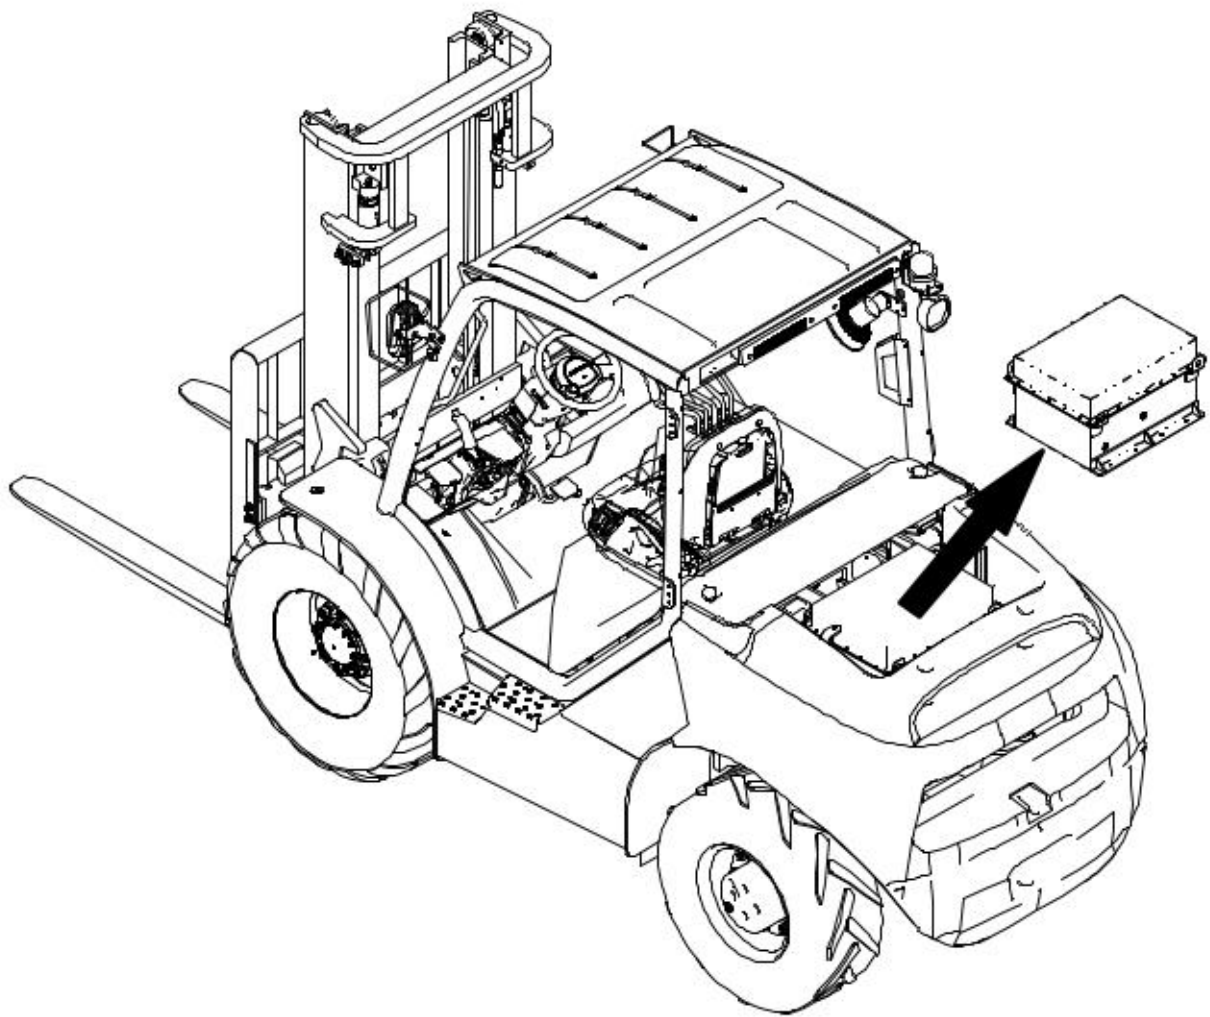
Heftruck krachtbatterijassemblage (slavebox)
